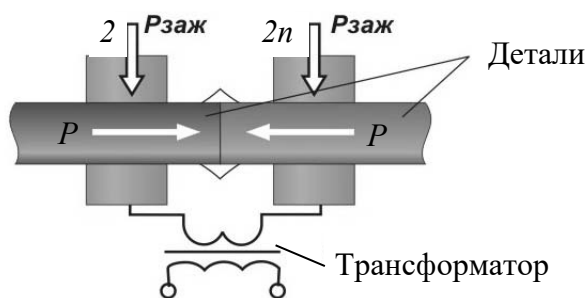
Схема стыковой сварки давлением
